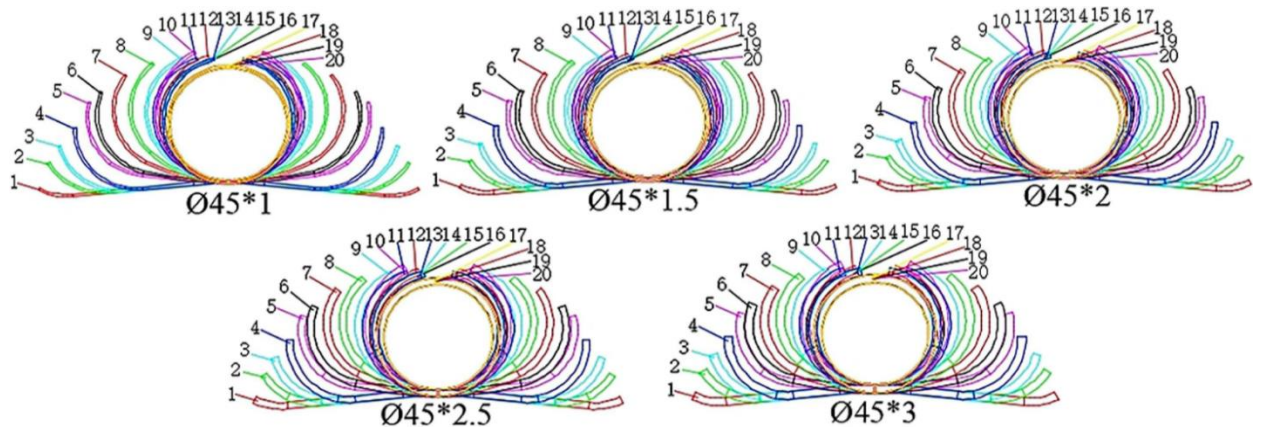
Схемы знакопеременной формовки сварных труб  $\text{Ø}45$  мм с различной толщиной стенки
